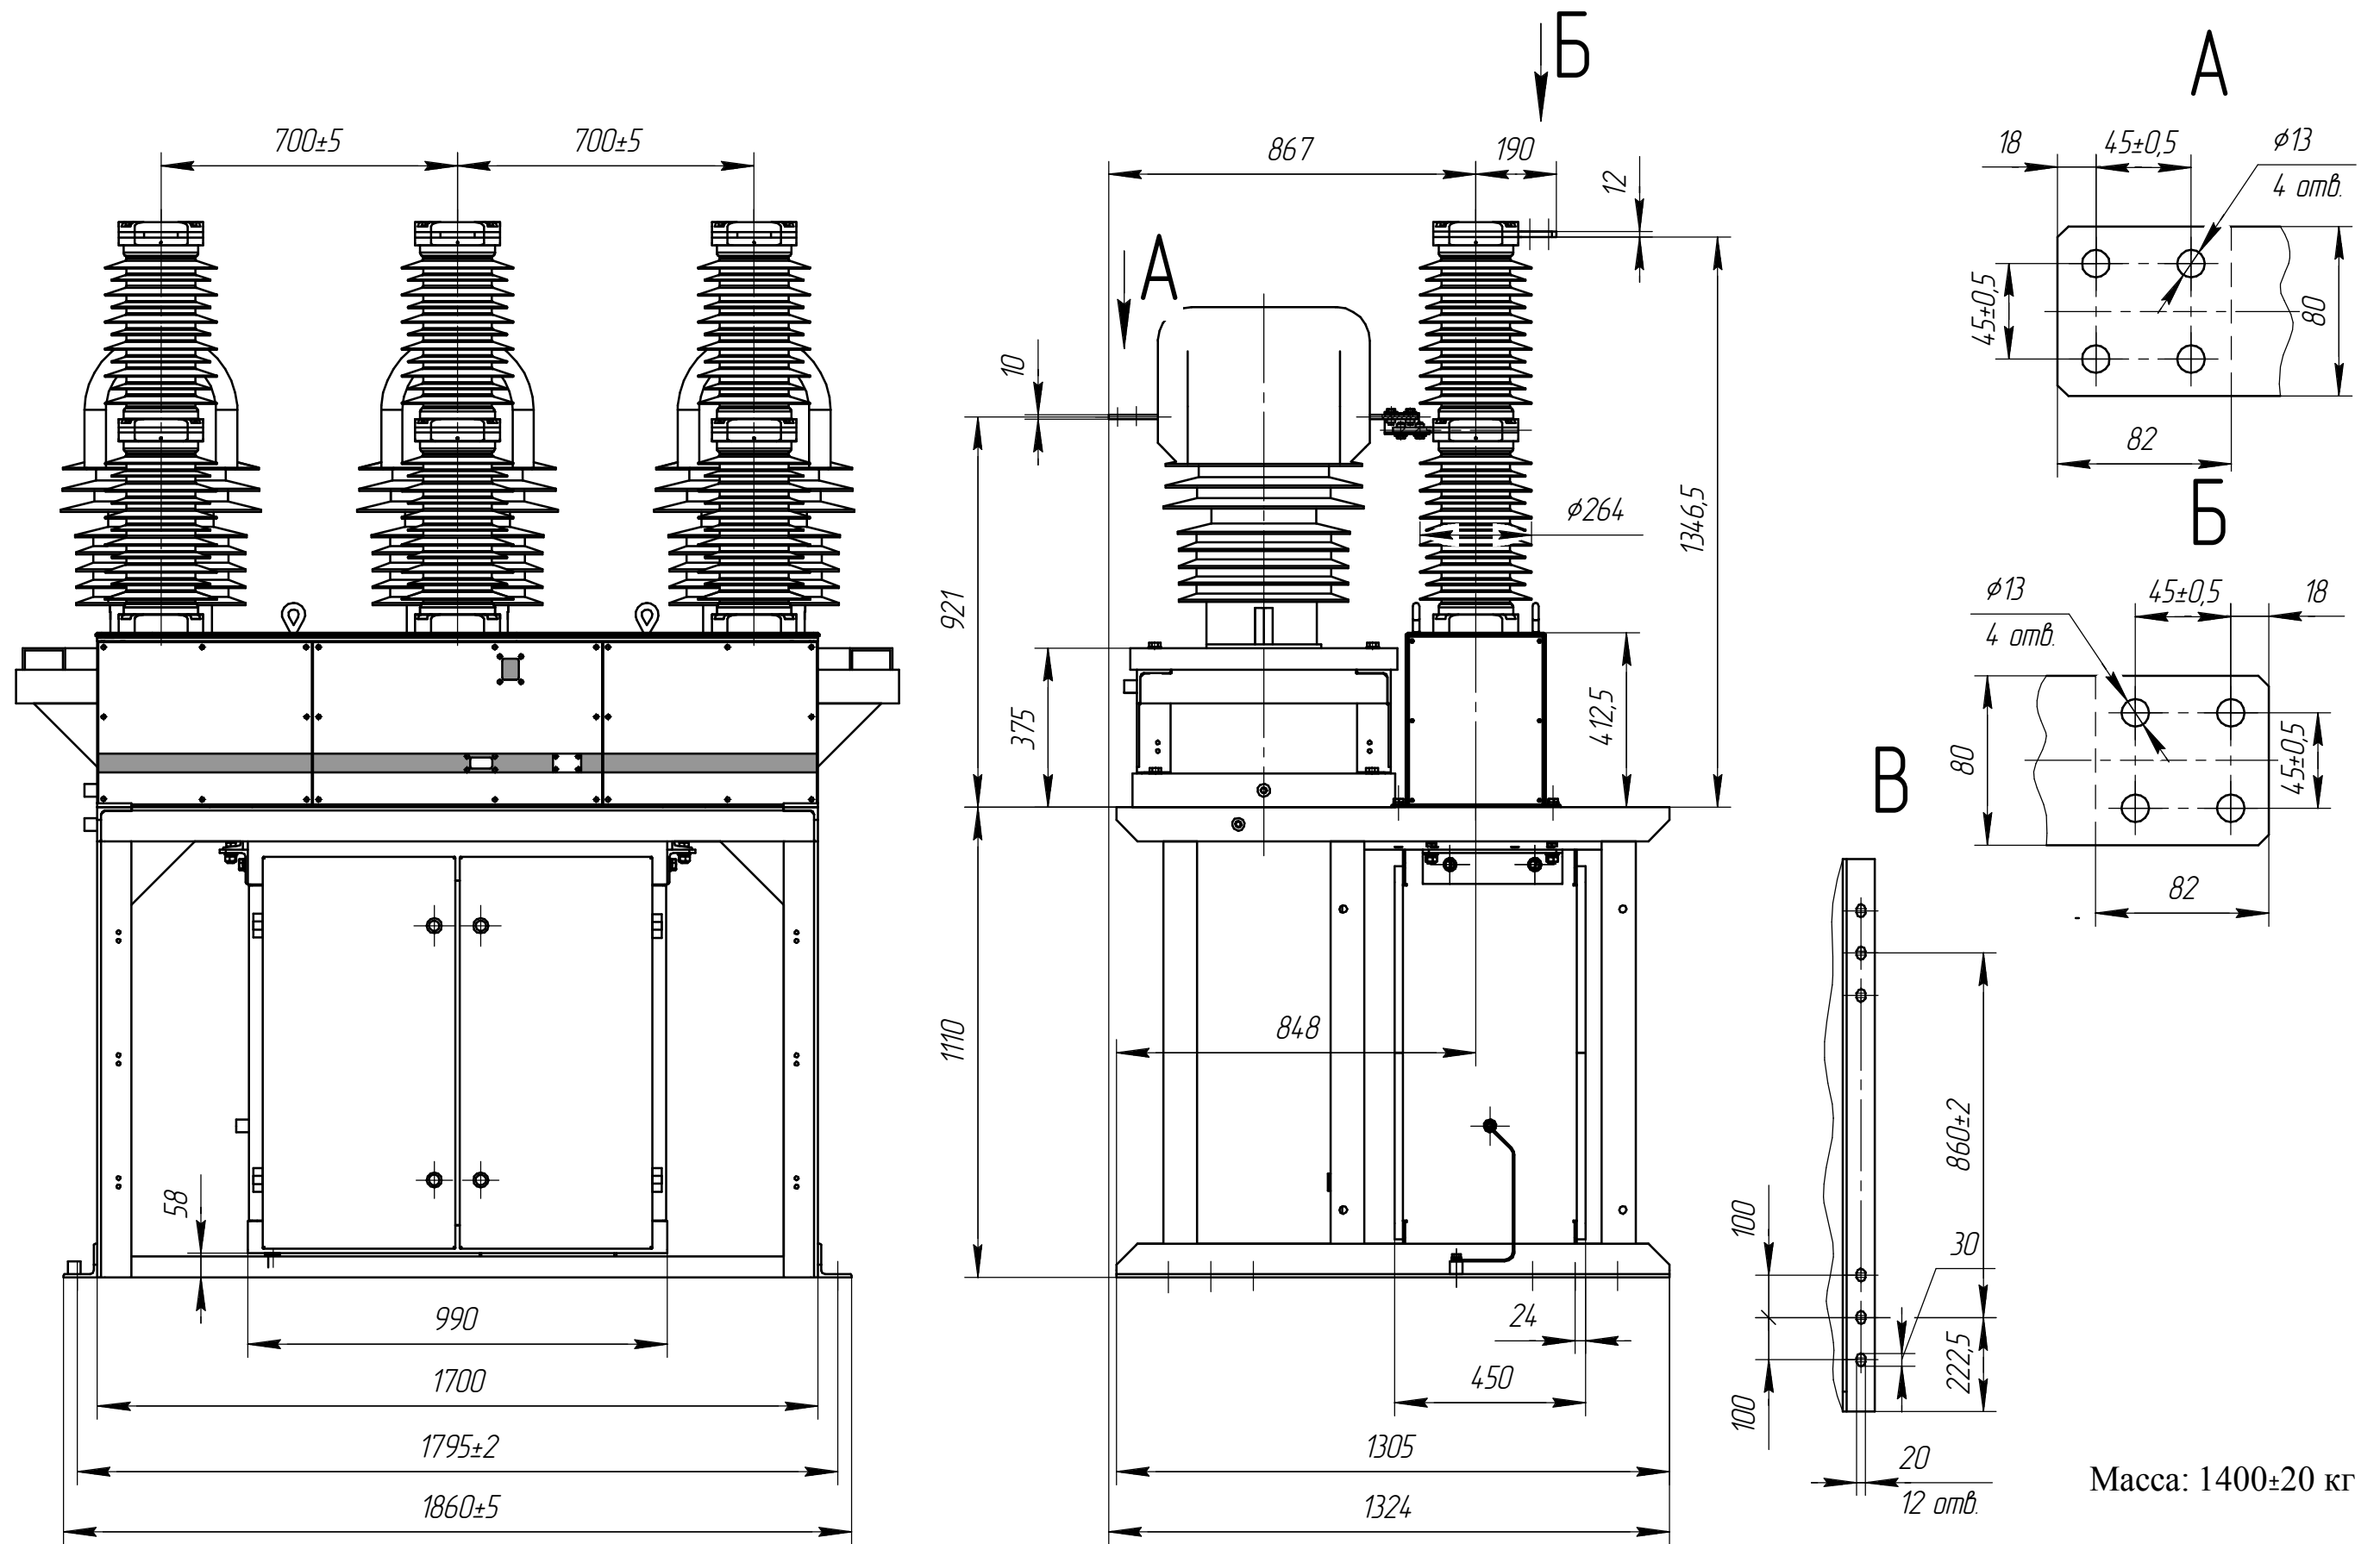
Габаритные, установочные и присоединительные размеры выключателя типоразмера ВР35НТ-35-25/1600-3/0 УХЛ1 с тремя встроенными трансформаторами тока ТОЛ-35 III-И УХЛ1 со стороны нижних контактов
